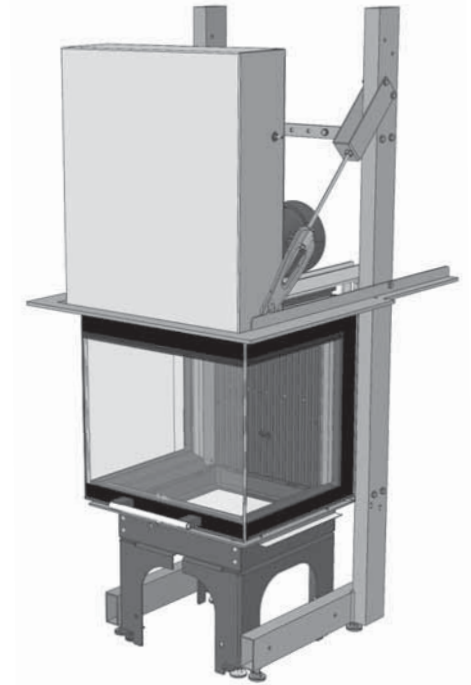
KALA QS mit Traggstell und angebautem Anbaurahmen oben
